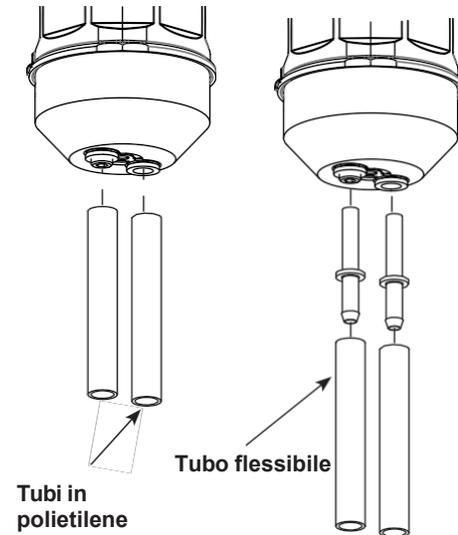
Assemblaggio dei tubi nel blocco Y inferiore
